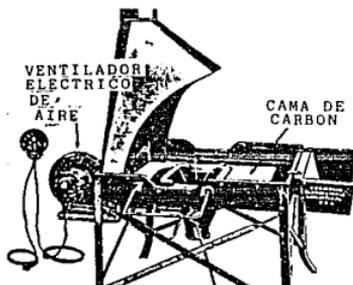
Forja de herrero usada para calentar metal para soldarlo por forja
